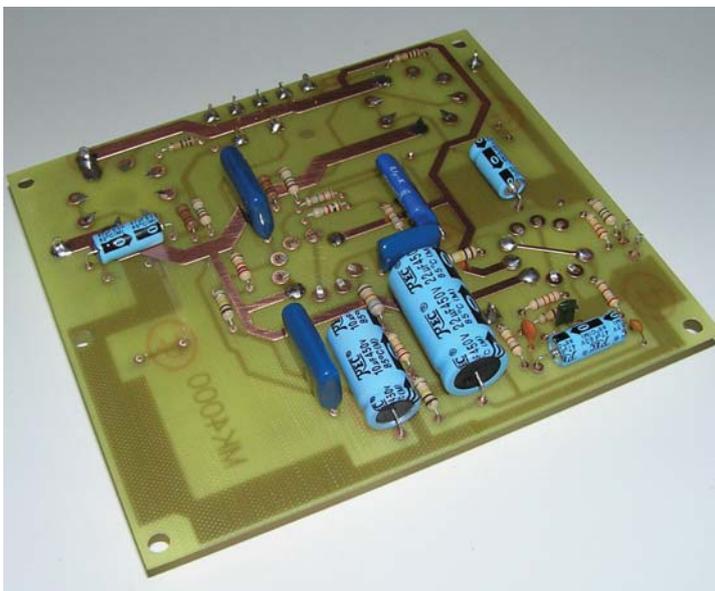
Plano de montaje lado soldaduras de la tarjeta MK4000
